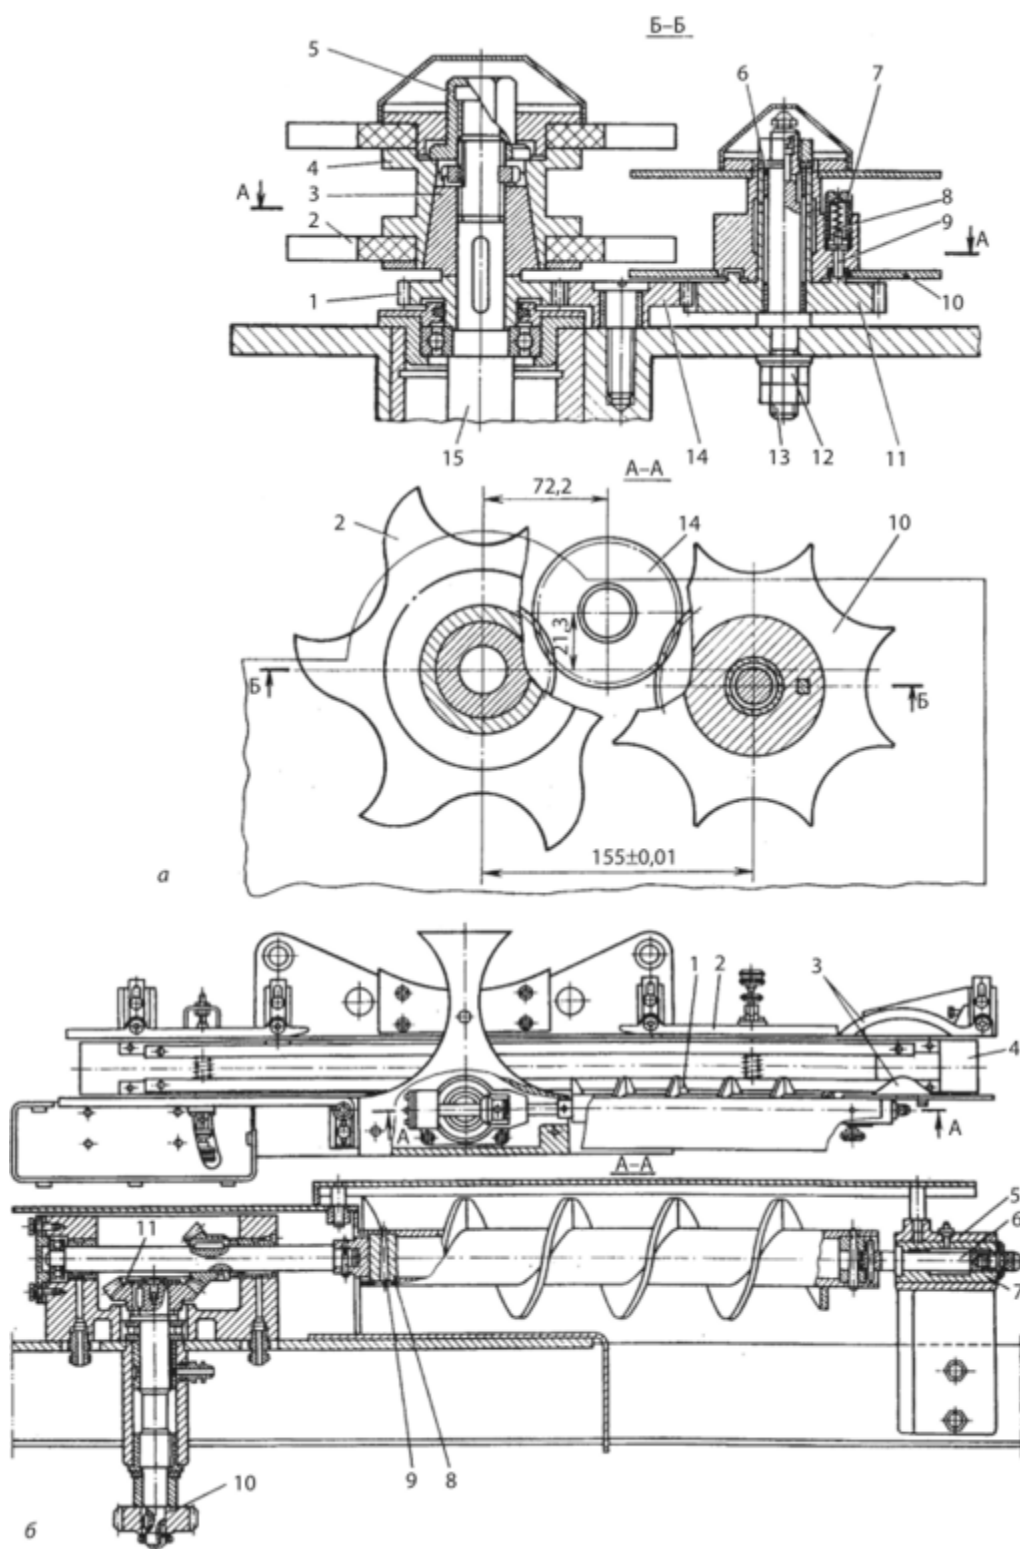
Ділильні пристрої фасувальних машин: а - ВАР-6: 1- зубчасте колесо; 2 - завантажувальна зірочка; 3 - конус; 4 - маточина; 5, 12 - гайки; 6 - підшипник ковзання; 7 - кант; 8 - пружина; 9 - фіксатор; 10 - ділильна зірочка; 11, 14 - шестерні; 13 - вісь; 15 - вал; б- Т1-ВРА-6: 1- шнек; 2 - огороження; 3 - перехідна гірка; 4 - конвеєр; 5 - корпус підшипника; 6 - вал; 7 - втулка; 8 - бобишка; 9 - штифт; 10, 11 - шестерні
